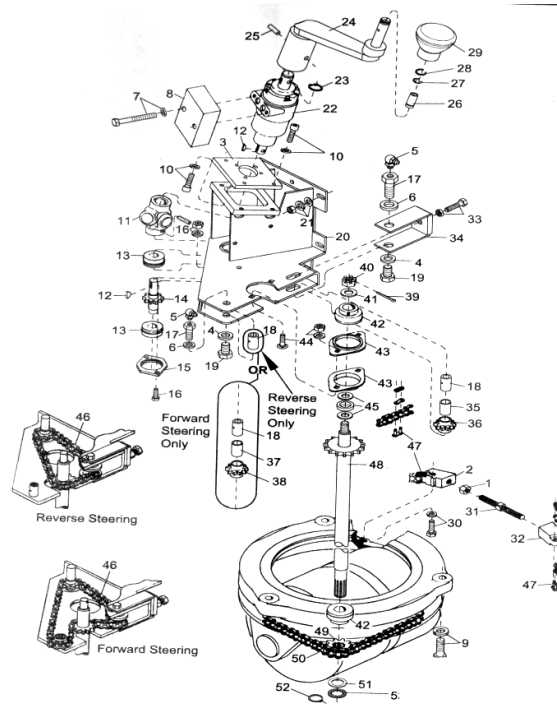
ENGRANAJE DE DIRECCIÓN
